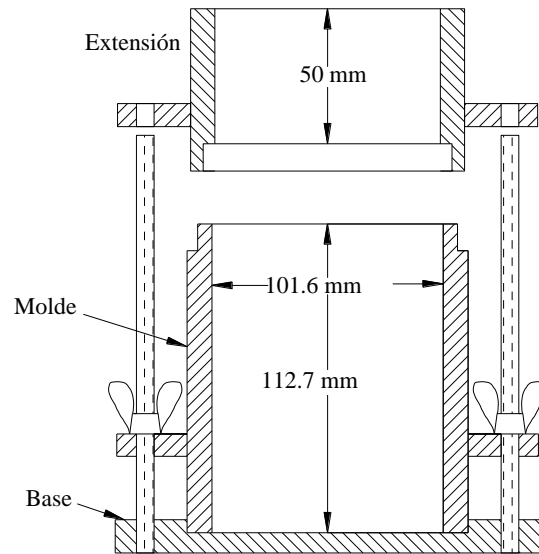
Dimensiones y partes del molde tipo Proctor.
